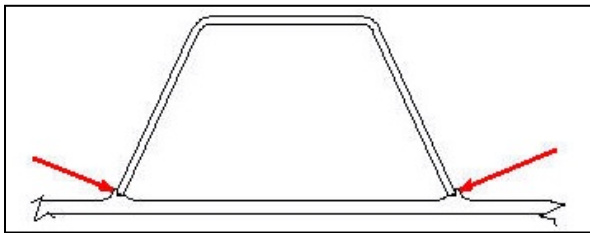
Beidseitig gleichzeitiges Laserstrahlschweißen von Hut-Stringern.
